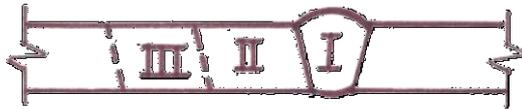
Зоны в сварном шве: I – шов (литая структура); II – околошовная зона, нагретая в процессе сварки выше критических точек; III – околошовная зона, нагретая в процессе сварки ниже критических точек
